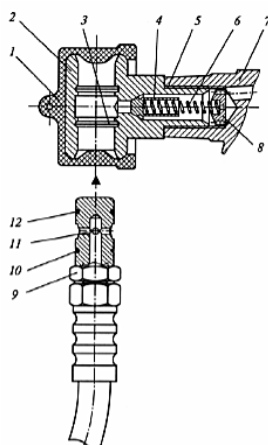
Выносной заправочный узел: 1 - защитный колпачок; 2 - штуцер заправочный; 3 - кольцевая канавка; 4 - обратный клапан; 5 - кольцо уплотнительное; 6 - пружина; 7 - корпус вентиля; 8 - упорный элемент; 9 - наконечник заправочного шланга; 10 и 12 - кольца распорные уплотнительные; 11 - канал подачи газа
